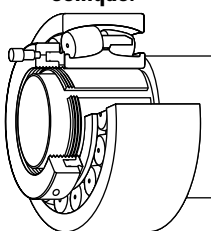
Écrou hydraulique utilisé pour monter le roulement sur un arbre cône.
